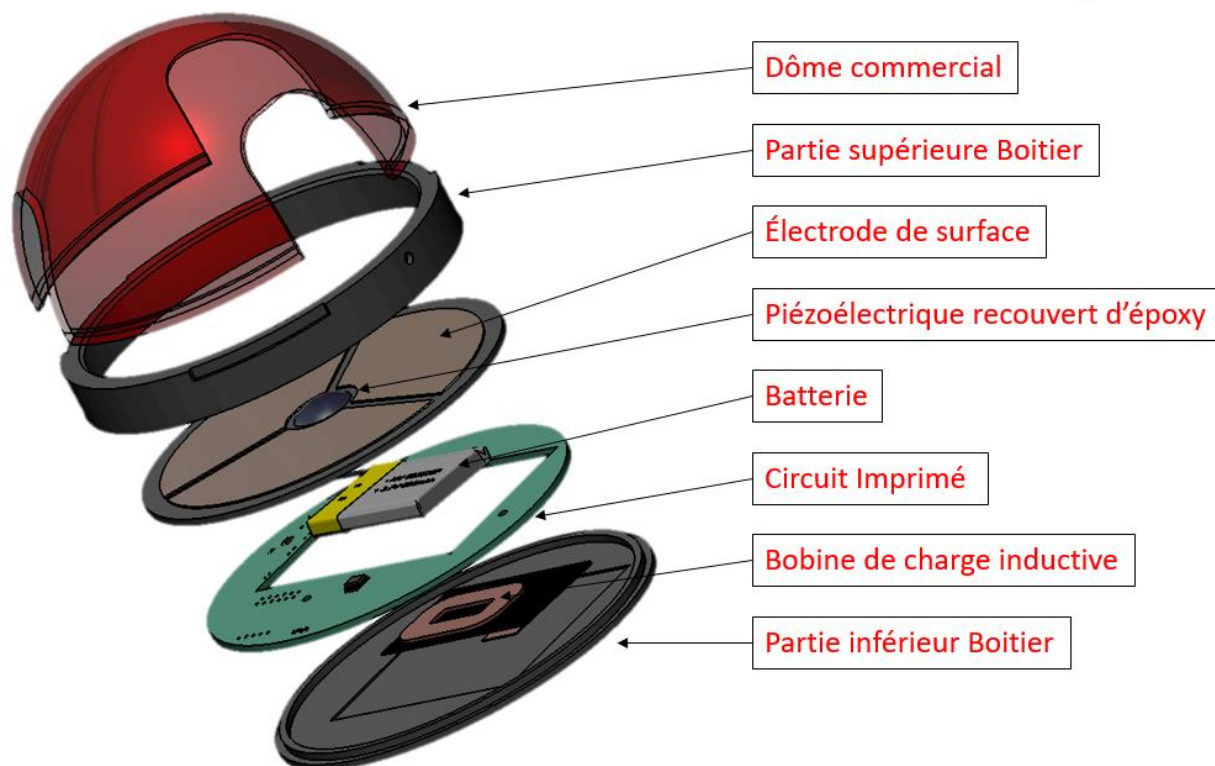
Vue explosé du système d'électrode de surface avec identification des pièces
